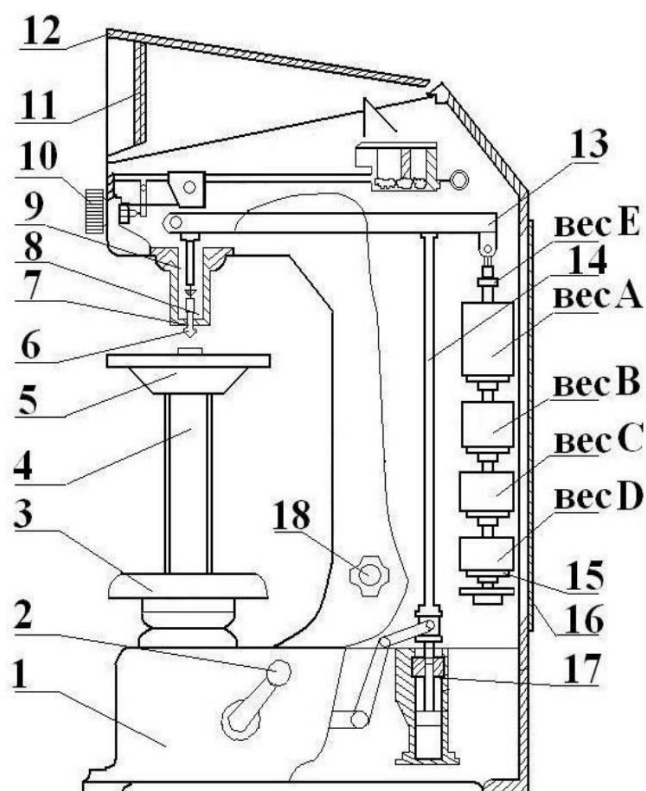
Общий вид стационарного твердомера HBRV-187.5 по шкале Бринелля, Роквелла и Виккерса:
